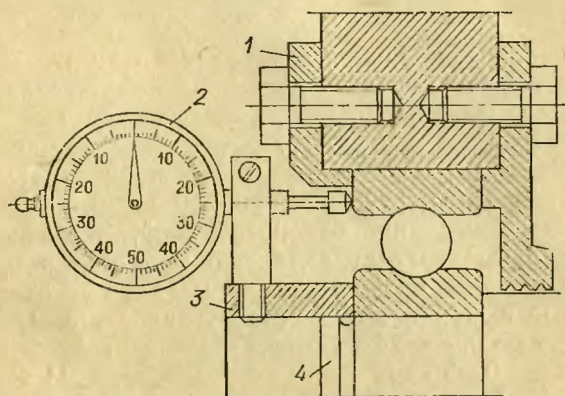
Приспособление для проверки правильности установки подшипников качения
